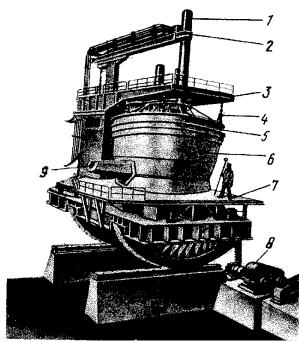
Дуговая сталеплавильная печь:1 - электрод; 2 - головка электрододержателя; 3 - свод; 4 - подвеска свода; 5 - сводовое кольцо; 6 - цилиндрический кожух; 7 - рабочая площадка; 8 -механизм наклона печи; 9 - желоб для слива стали
